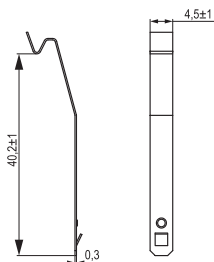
Габаритные и установочные размеры скобы / Figure 7 - Overall and mounting dimensions of the bracket / 7 сурет – Қапсырғыштың габариттік және орнату өлшемдері CRS-G-1
